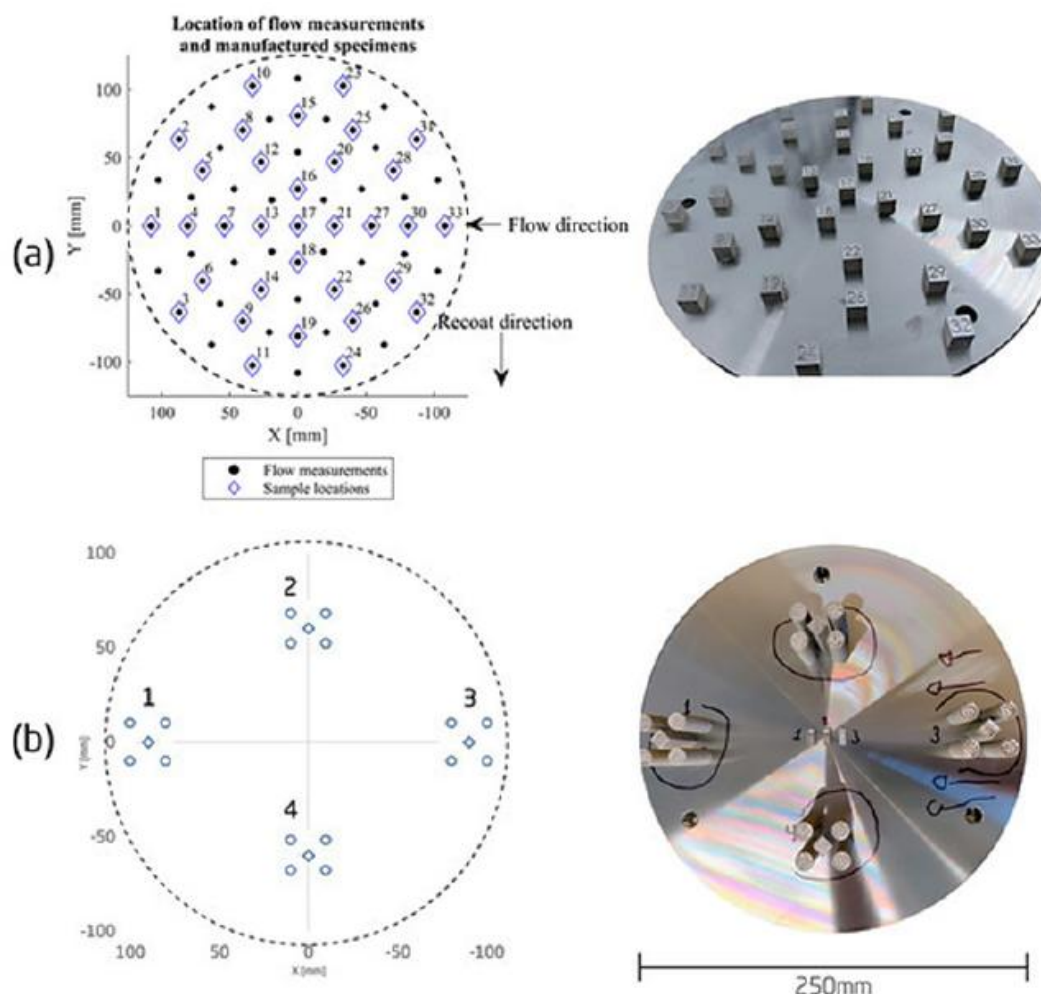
Фото и схема местоположения и направления газовых потоков, а также размещение образцов:
